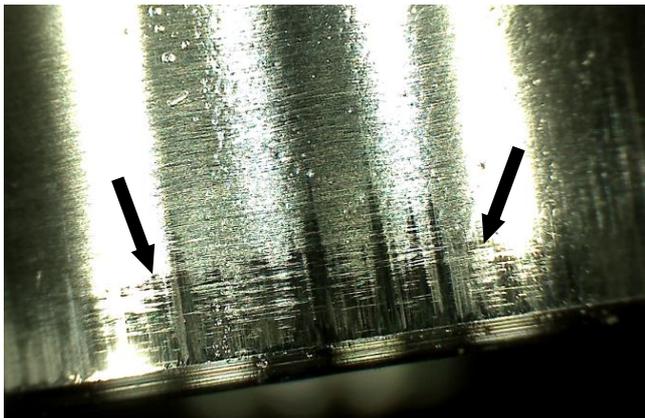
Натирь на наружной цилиндрической поверхности толкателя плунжера ТНВД
